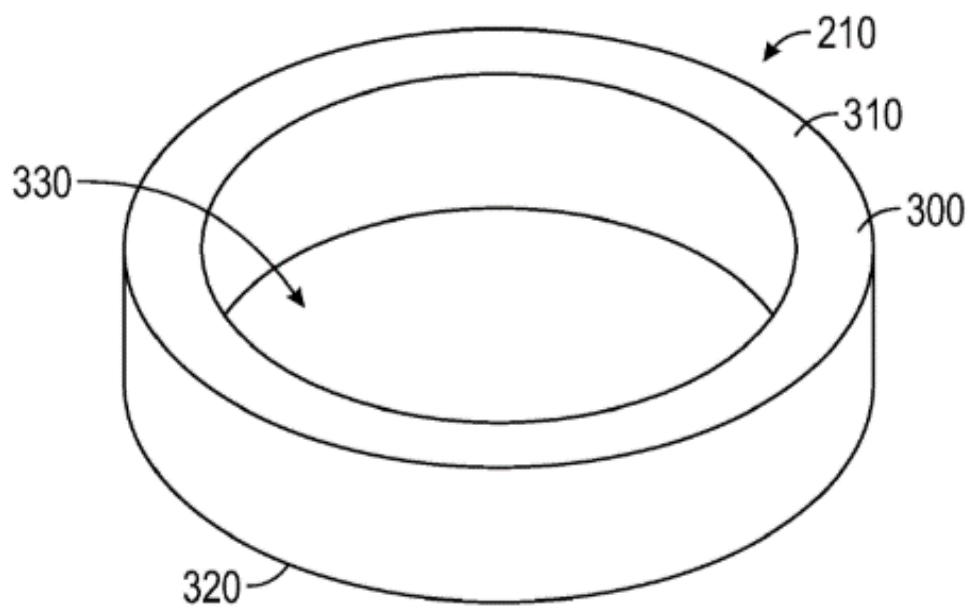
монтажне кільце вала-шестерні конусної дробарки:
